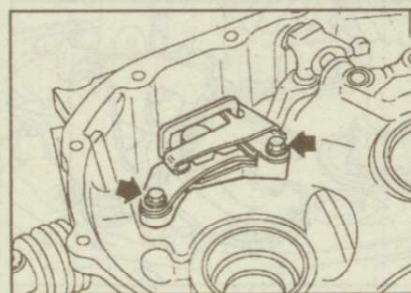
Установочное положение заслонки передачи заднего хода
